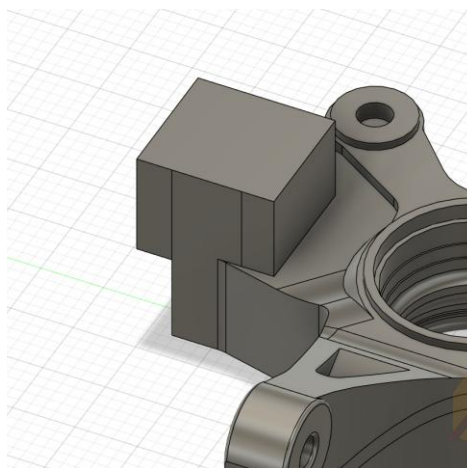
Modelado CAD – Extrusión Rótula Inferior (Elaboración Propia)
